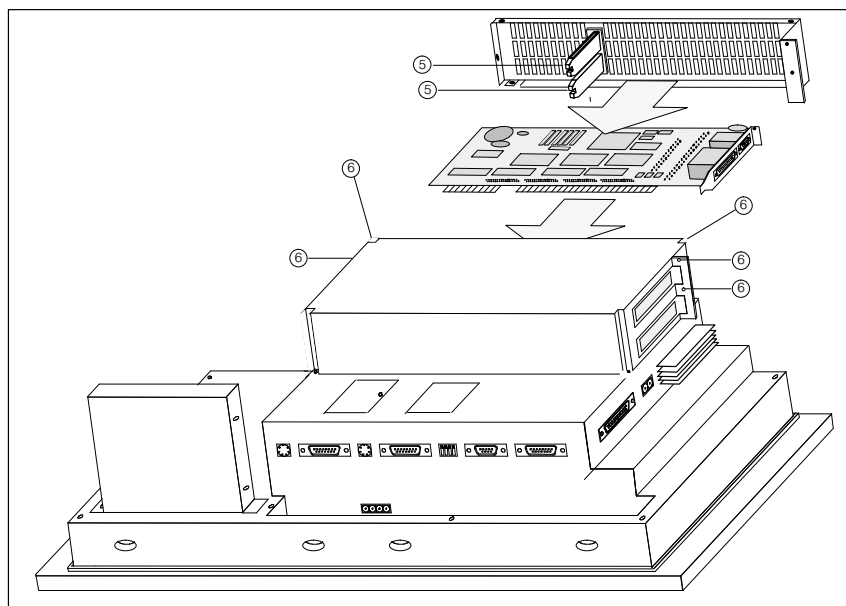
AT-Karte stecken und Seitenteil befestigen
